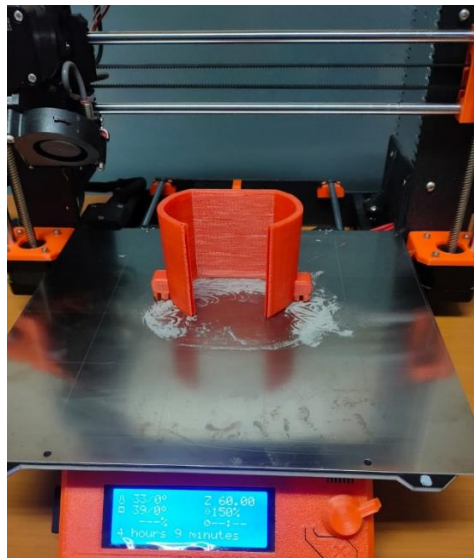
Impresión 3D por impresión por deposición de material [Fuente Propia]
